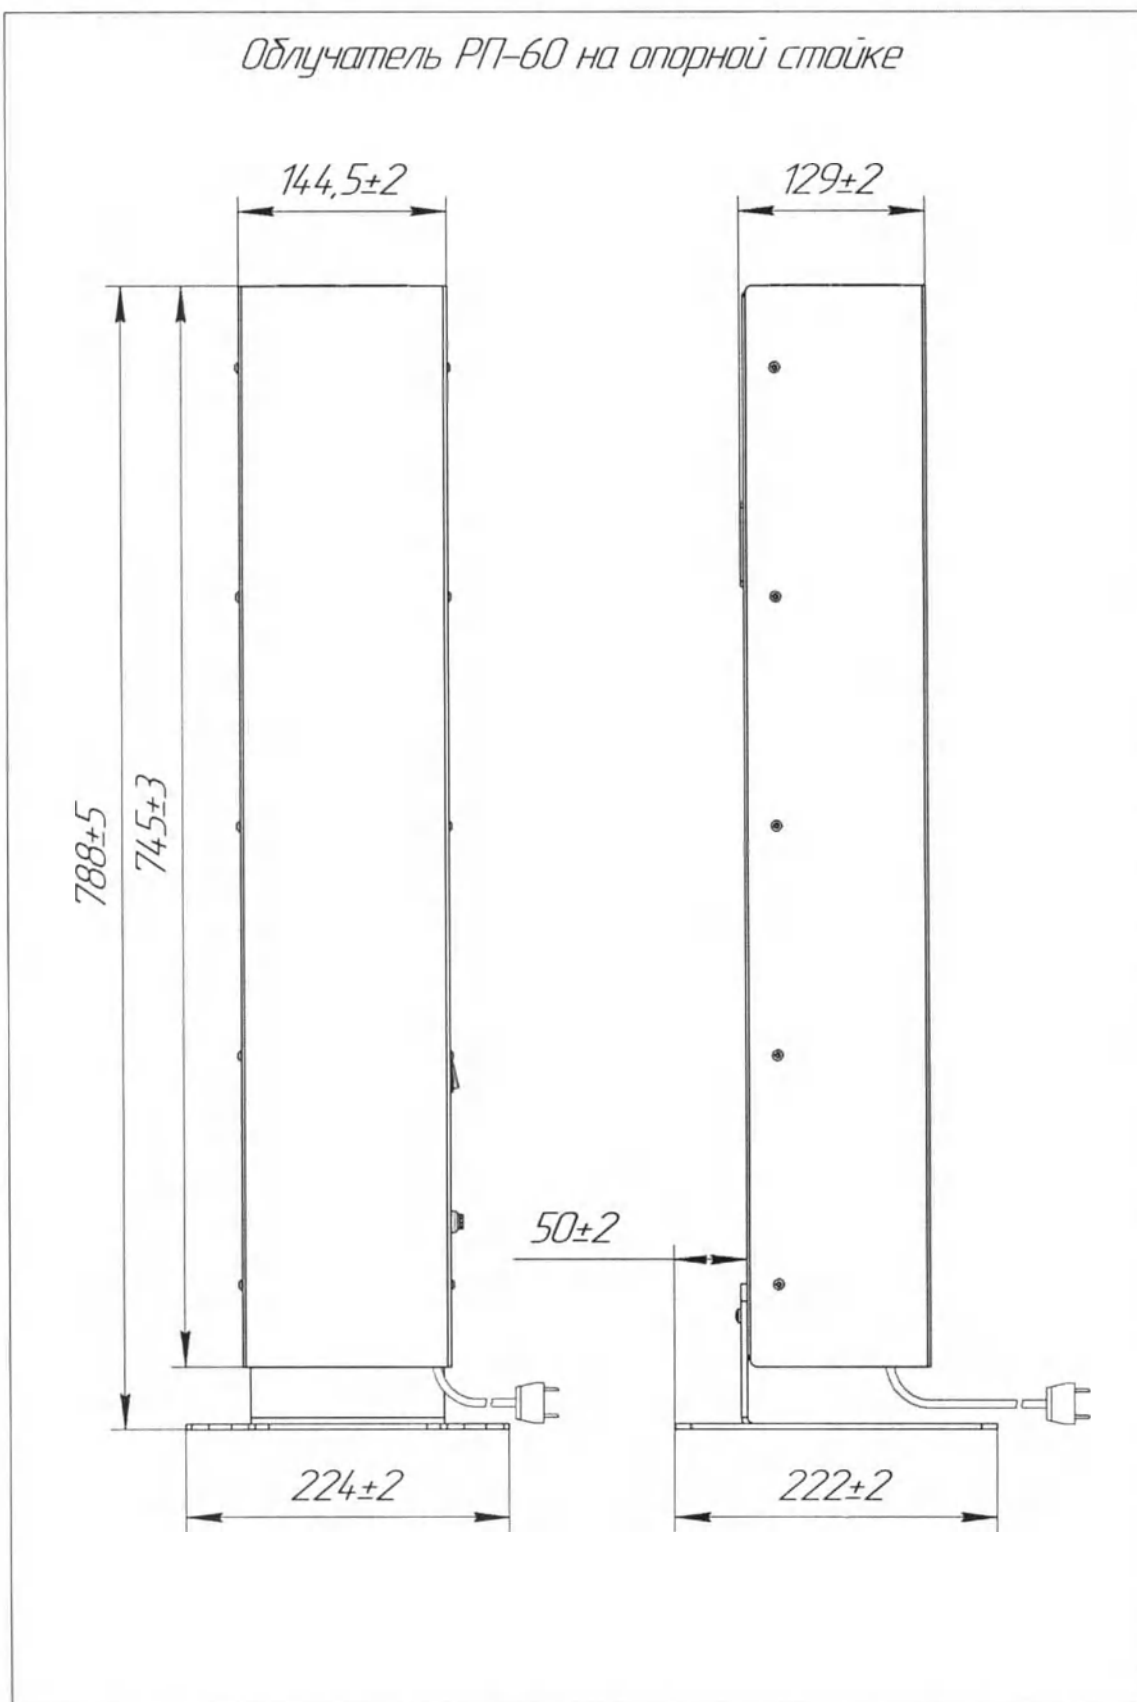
Облучатель РП-60 смонтированный на опорную стойку
